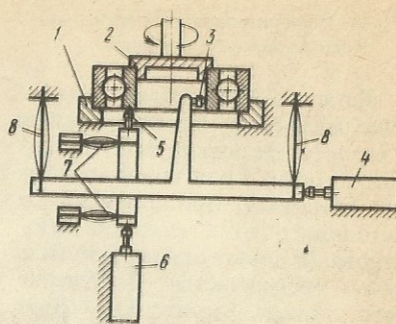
Компоновка контрольной позиции автомата для проверки биения шарикоподшипника
